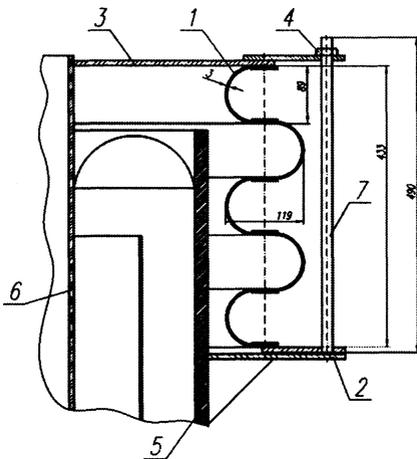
Схема компенсатора: 1 - рабочий элемент компенсатора; 2 - опорный фланец; 3 - кольцо; 4 - гайка; 5 - корпус вагранки; 6 - тепловоспринимающий корпус рекуператора; 7 - шпилька
